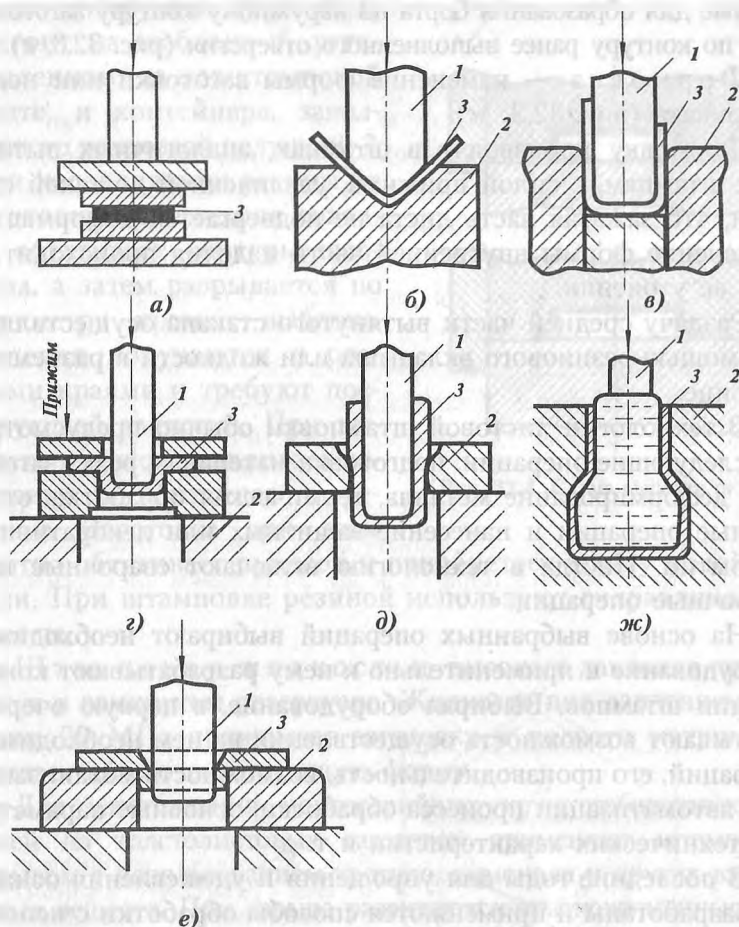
Формоизменяющие операции листовой штамповки: 1 — пуансоны; 2 — матрицы; 3 — изделия или полуфабрикаты
